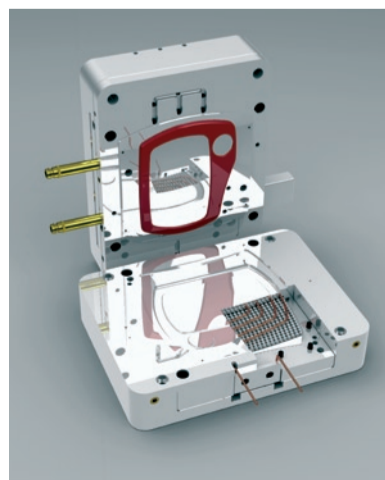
Werkzeugeinsatz mit 3iTech® und BFMOLD™-Technologie
